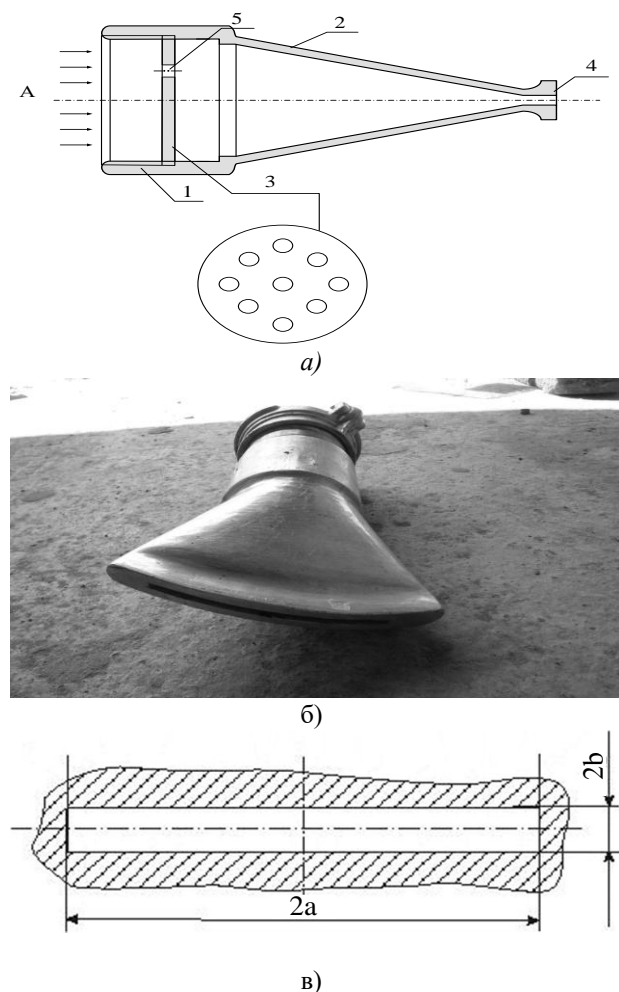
Общий вид насадка-дефлектора для создания веерной струи: а) – вид устройства в разрезе; б) – фото устройства со стороны щелевого проема; в) размеры выходного сечения одного из натуральных образцов ствола-распылителя радиальных веерных струй: $2a = 140$ мм; $2b = 3$ мм
